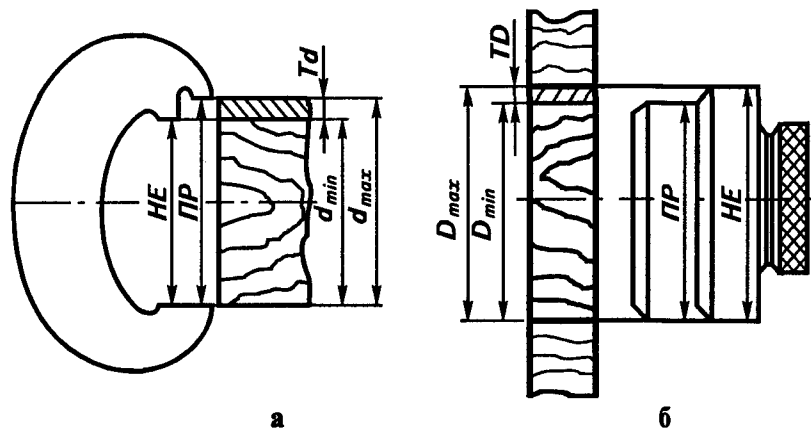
Калибры: а — калибр-скоба для контроля вала; б — калибр-пробка для контроля отверстия
